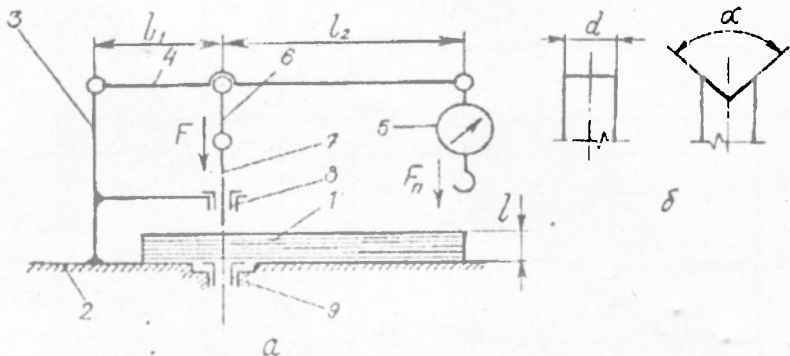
Пристрій для перфорування отворів: а — схема; б — форми робочої поверхні пуансонів.
